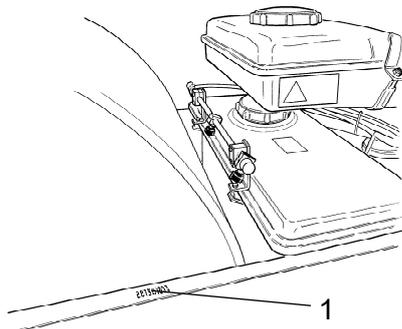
PIN (numéro d'identification du produit), châssis arrière
